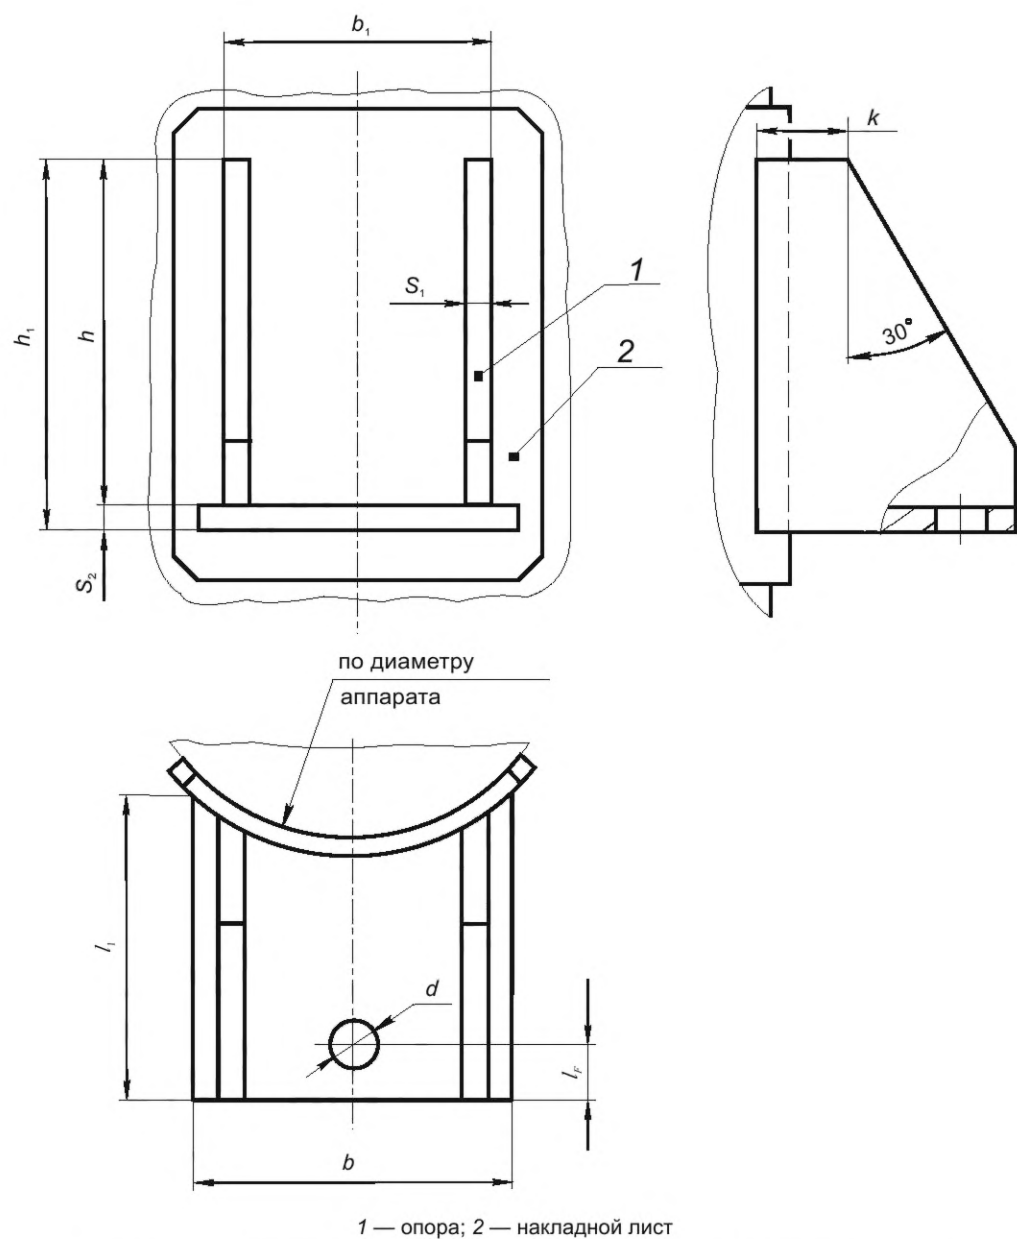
Типовая конструкция сварной опоры вида «Л» (исполнения 2, 4)
